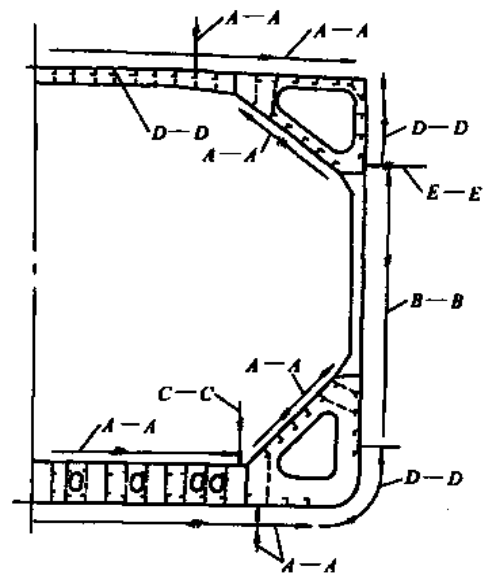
16500m³ 液化气船船体大合拢焊接方法
